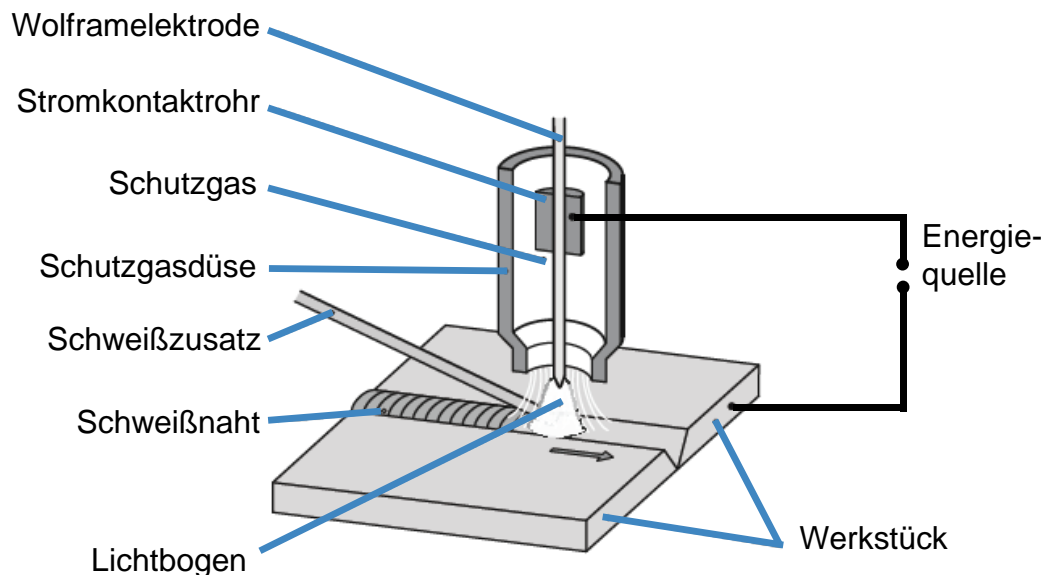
Grundprinzip des Metall-Schutzgasschweißens [41]
